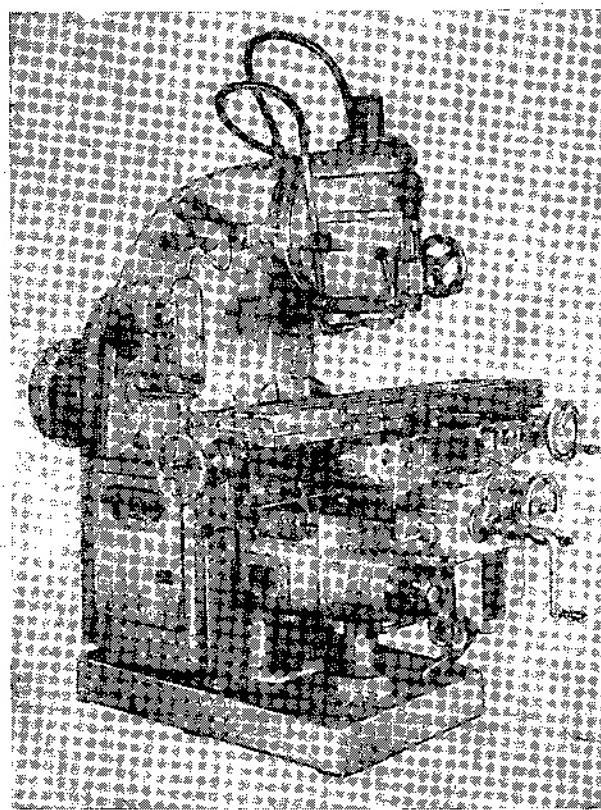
Вертикальный консольно-фрезерный станок с поворотной головкой модели 6М12П
